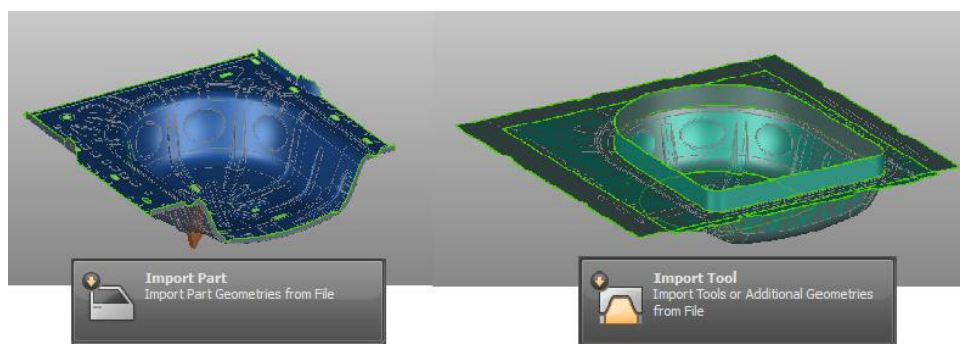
Импорт детали и рабочей оснастки в Autoform
